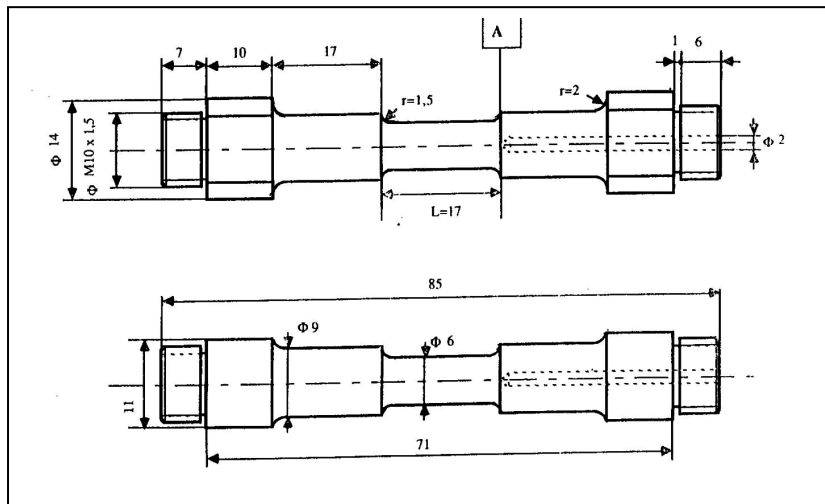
Géométrie des éprouvettes longitudinales (dimensions en mm)
